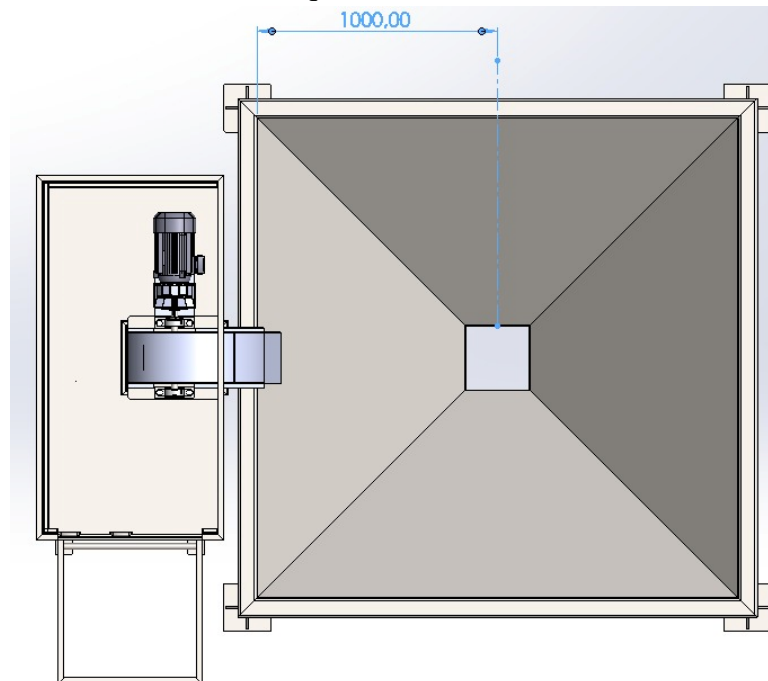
Vista en planta de tolva y elevador a cangilones. Apreciación de la distancia entre las bocas de descarga de ambos equipos.
